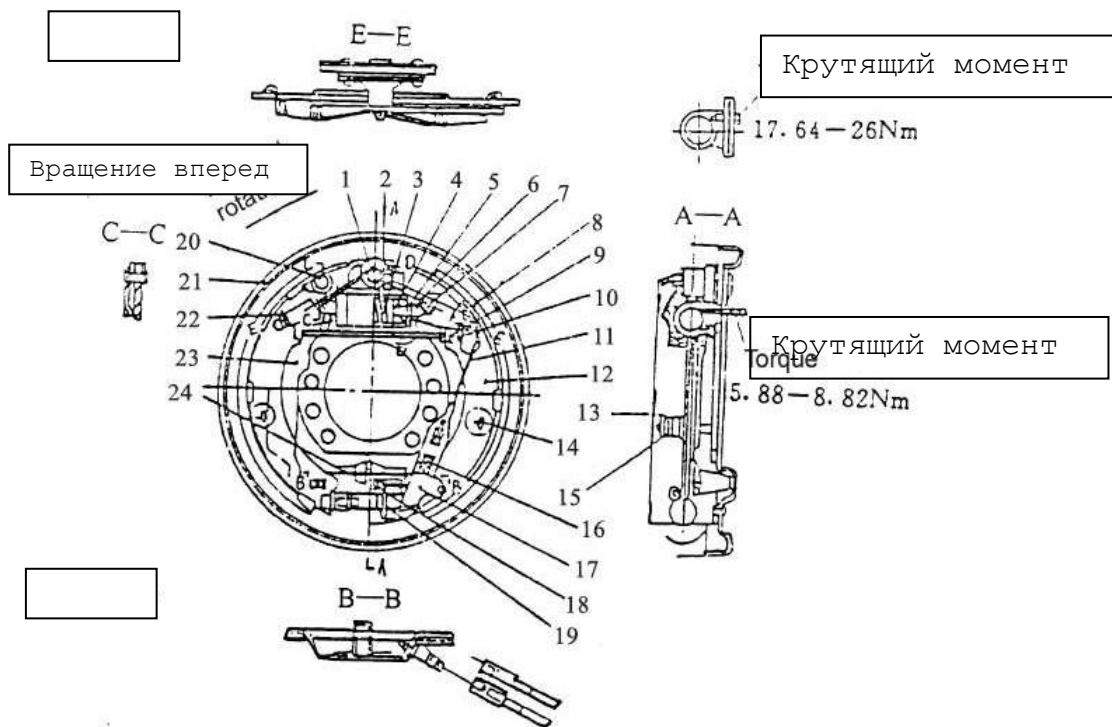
Колесный тормоз для погрузчиков 3 и 3,5 т:
